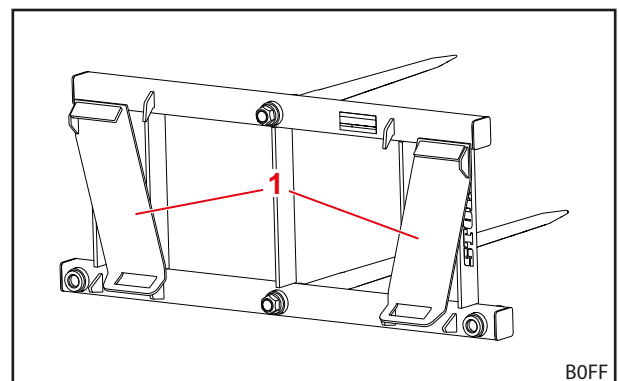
Aufbau Ballenspieß Skid – Rückansicht
